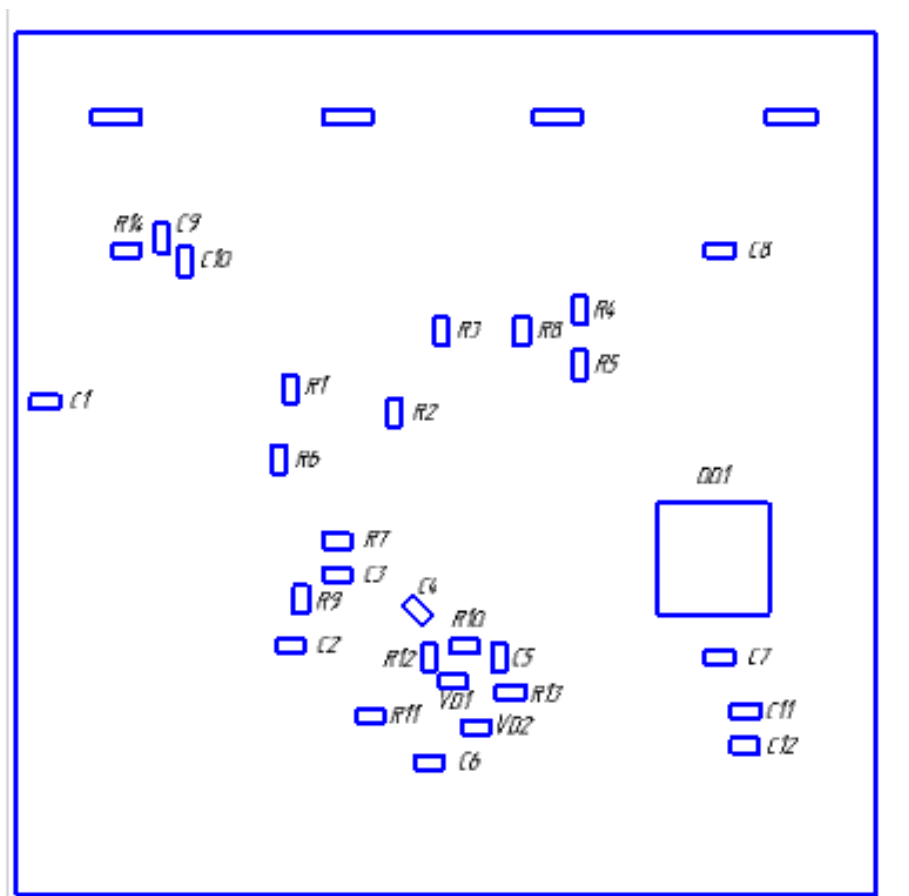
Розташування елементів поверхневого монтажу на платі керування
